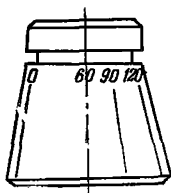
Съемная насадка гайковерта с нанесенными рисками для контроля угла поворота гайки на 60, 90 и 120°
